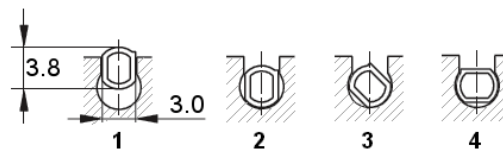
Sensor von oben in die Nut senkrecht einschieben.
